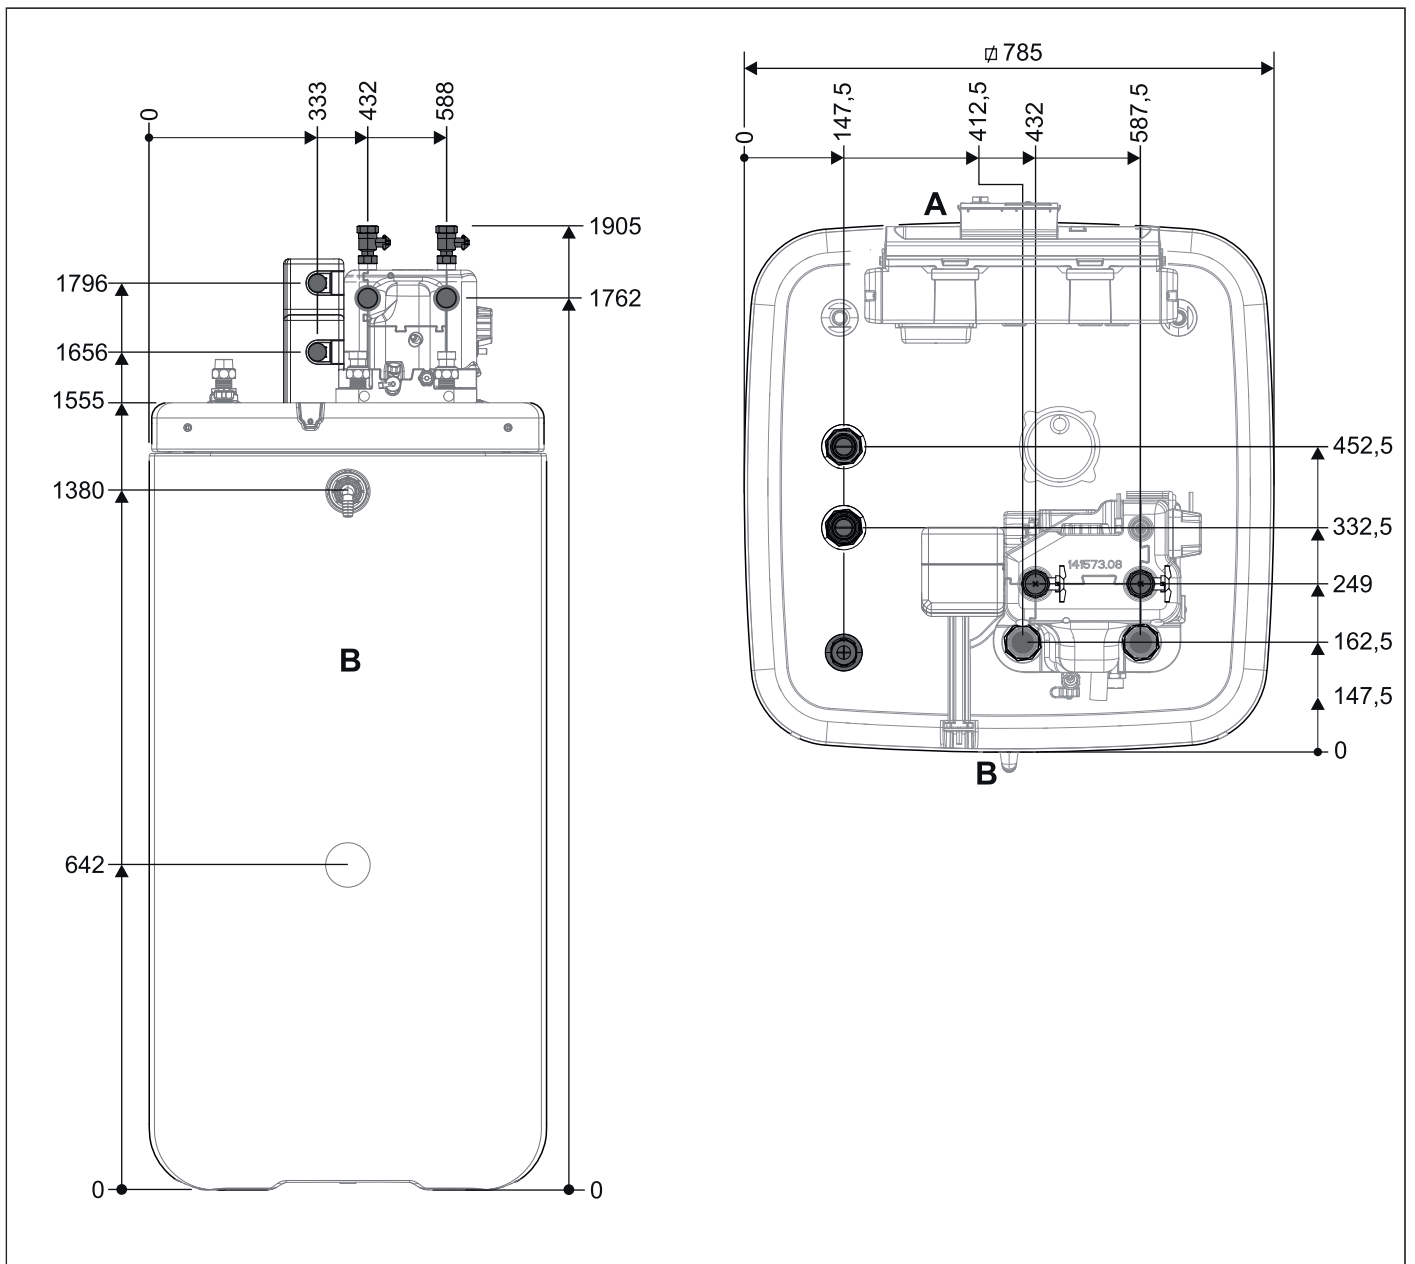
Anschlüsse und Abmessungen RKHWMX(B)500C
